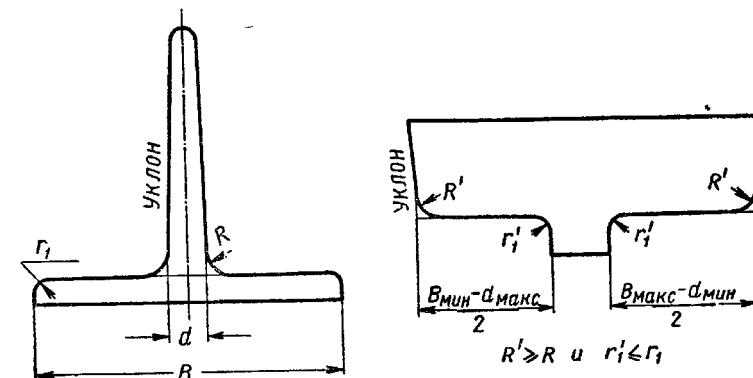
Готовый профиль тавровой стали и контрольный шаблон для замера симметричности полок
